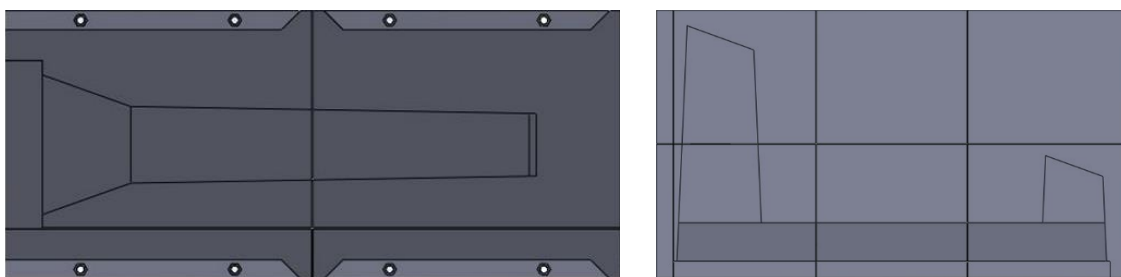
Diseño del molde: Interior del molde (izda). Diseño en alzada (dcha).
